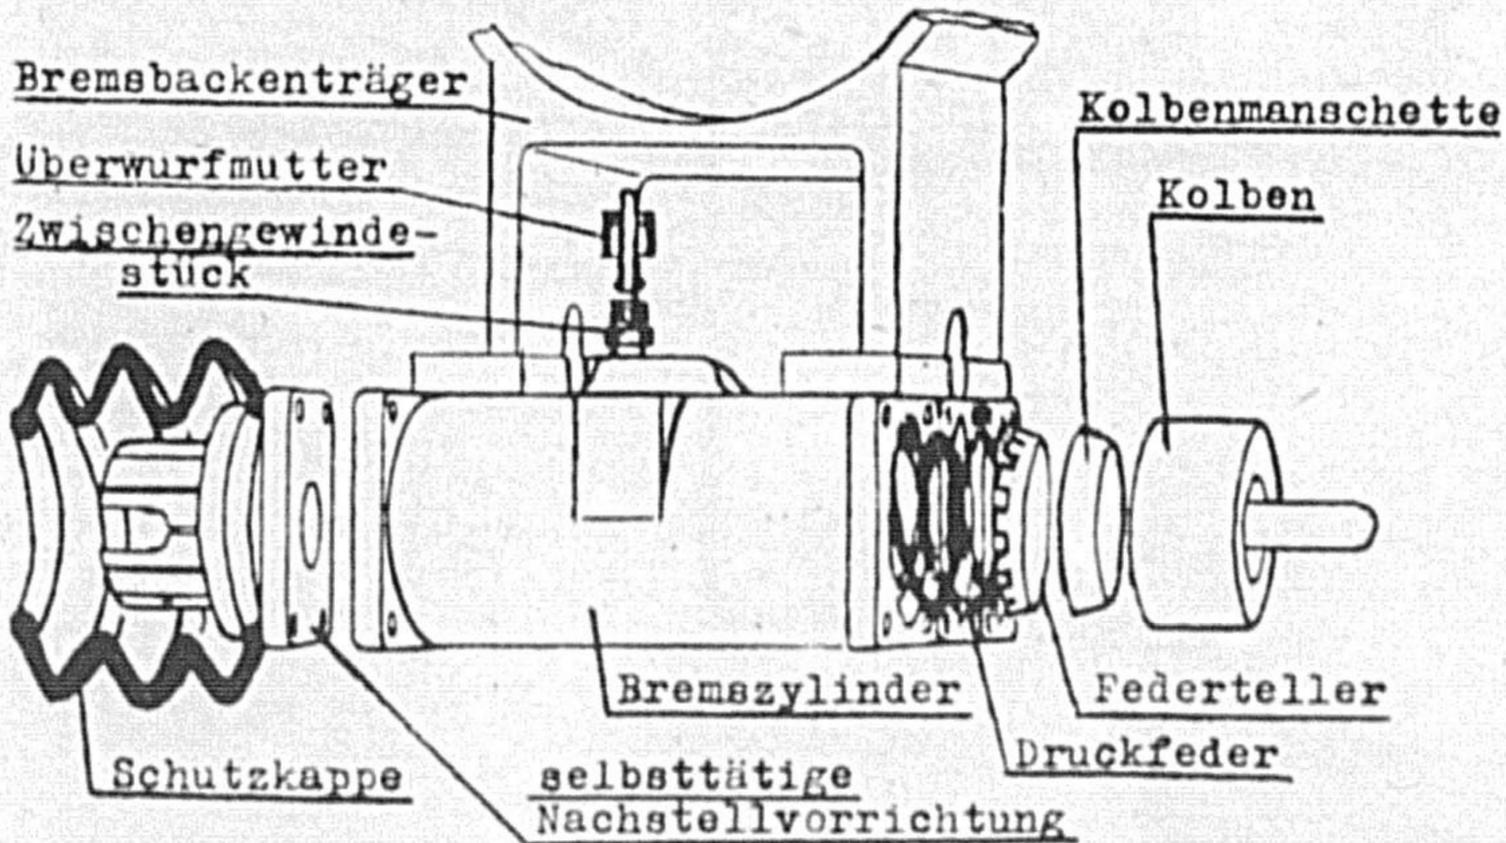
Lösen der Bremsölleitungen, der Halteschrauben und der Deckelschrauben an den Bremszylindern. Zerlegen der Bremszylinder
